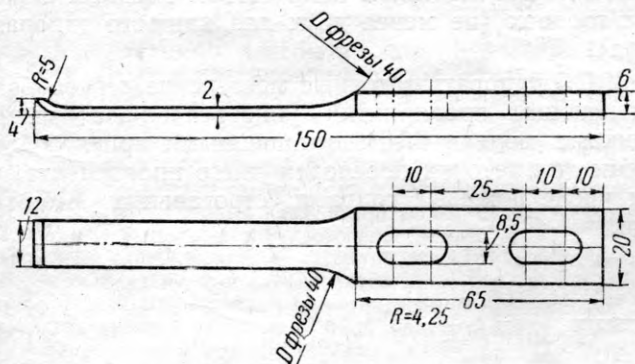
Общий вид упорки для фиксации ножевой головки фуговального станка
